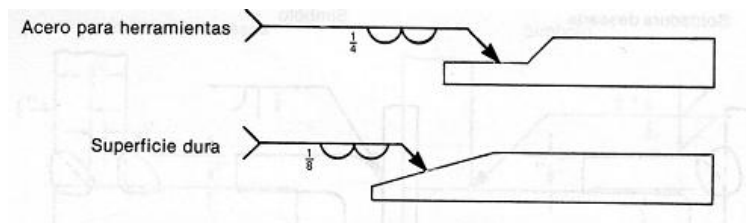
Símbolos de soldadura en los que se especifica la altura máxima de engruesamiento de una superficie que va a ser recubierta.
